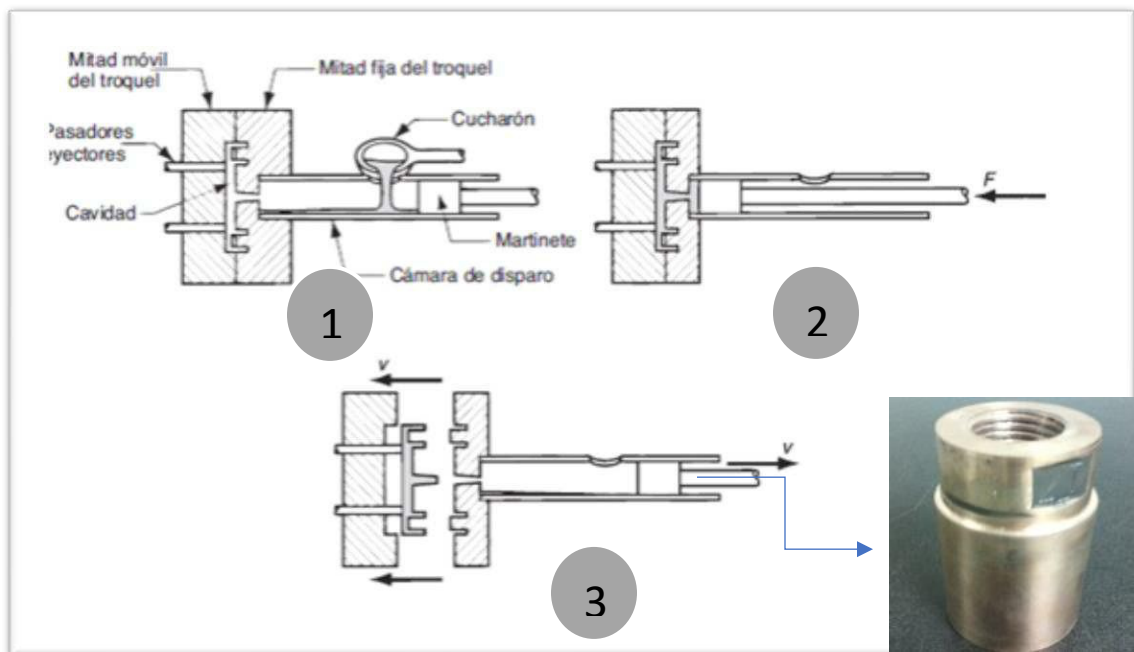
Extracción de la pieza fundida fuera del molde, empujada por los botadores.
